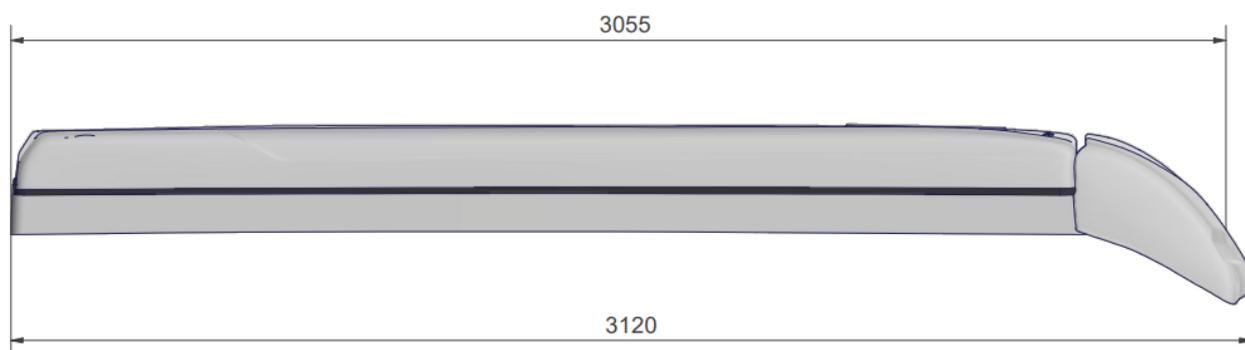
Universal roof Maxi-Van [G0001550]
